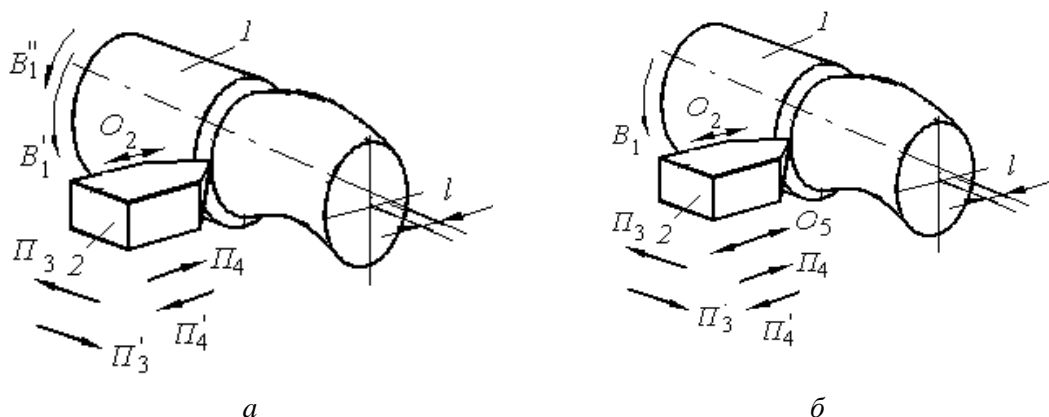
Схемы точения круговой винтовой поверхности при сообщении дополнительного движения заготовке (а) или резцу (б)
